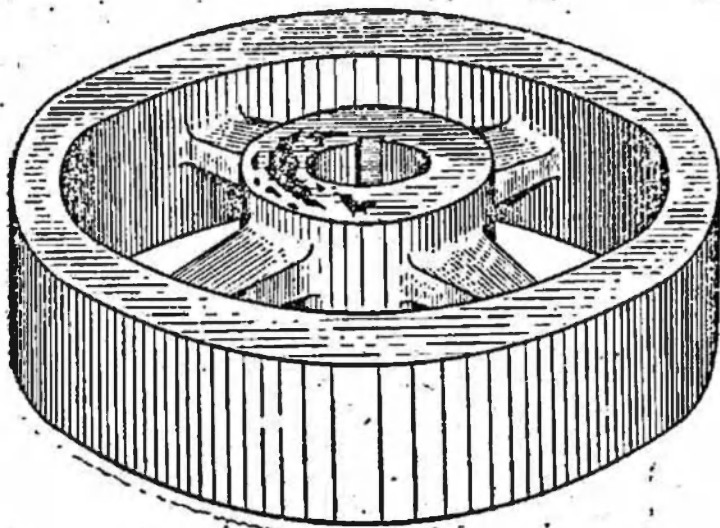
Размеры отливки меньше размеров детали, и на детали при ее механической обработке остались черновины.
